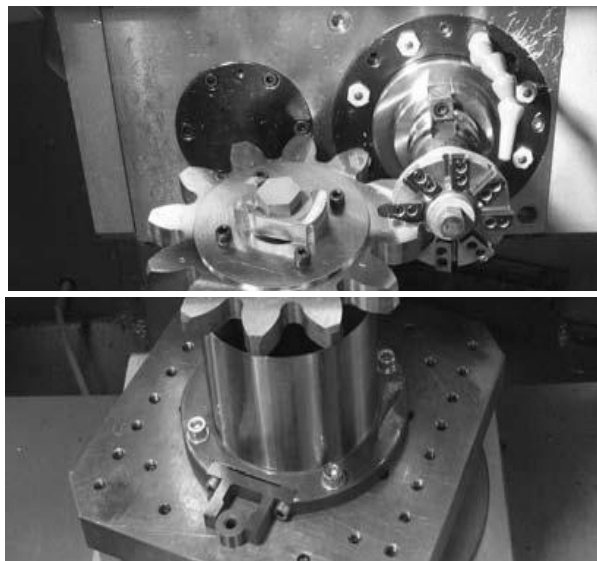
Нарізання зубчастого колеса на горизонтальному фрезерному верстаті з ЧПК за методом контурного оброблення
